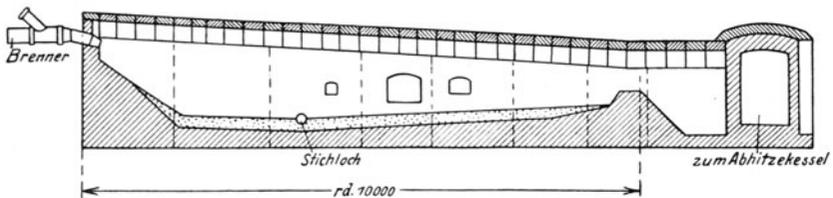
Flammofen neuerer Bauart (Grindie Fuel Equipment Co.).
